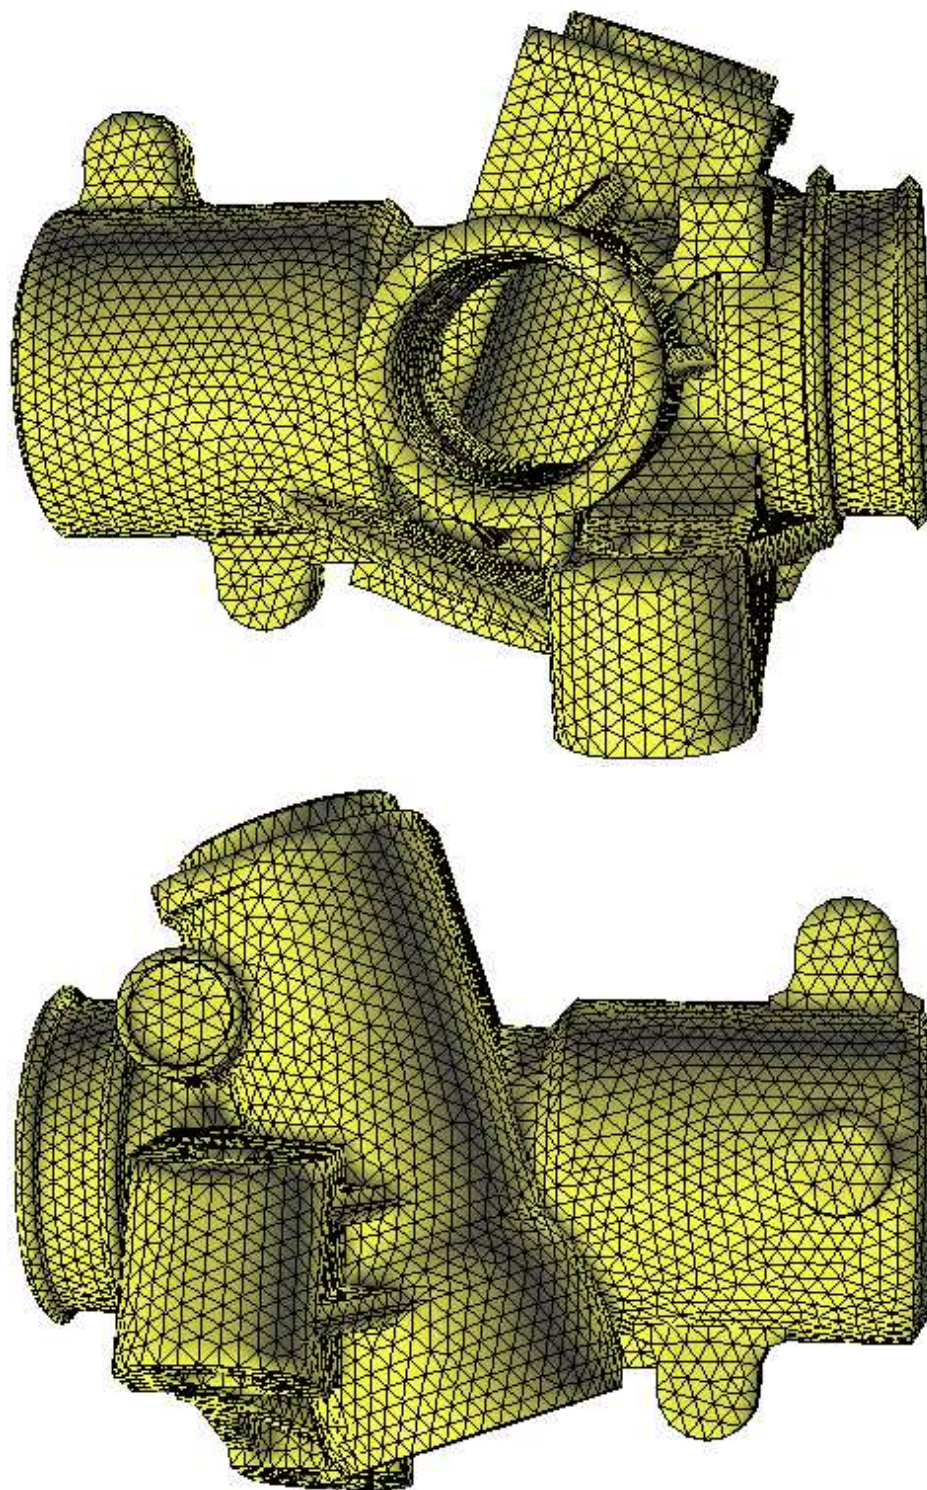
Surface PSA : vue de chaque côtés de la pièce.
